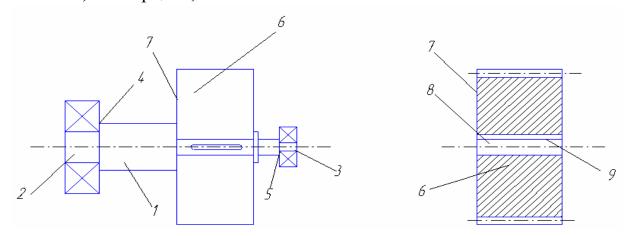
Схема, поясняющая суть конструкторских баз
